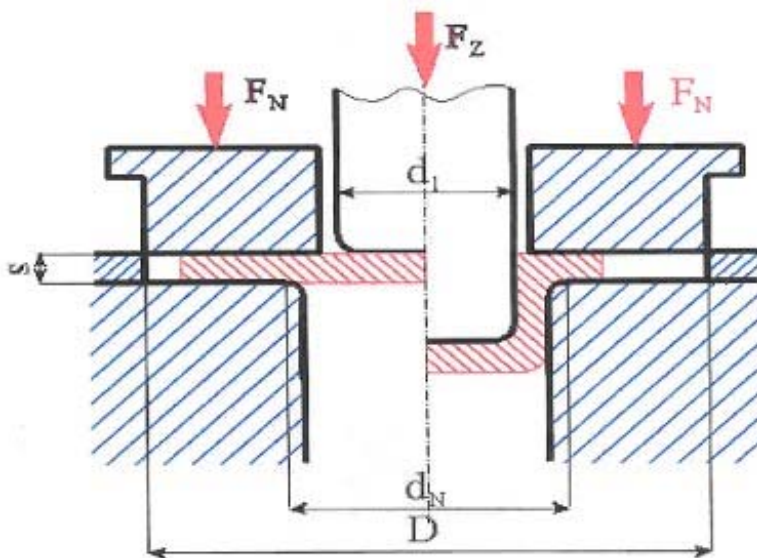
zu den Geometrien des Tiefziehwerkzeuges
